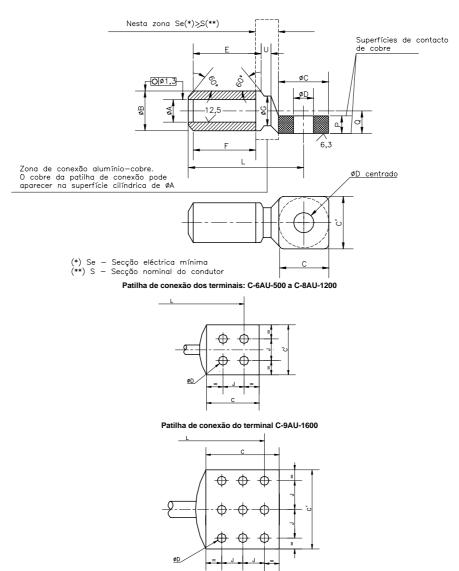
Dimensões dos terminais bimetálicos alumínio-cobre
